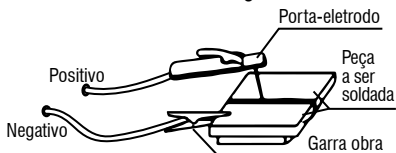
Montagem dos cabos de solda para soldagem de Eletrodo Revestido (MMA)
